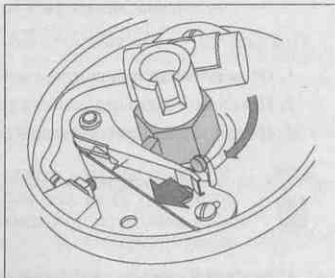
Двигатель прокручивается до тех пор, пока подушечка кулачка прерывателя не попадет на утолщение кулачка прерывателя. Это придает контактам прерывателя наибольший зазор
